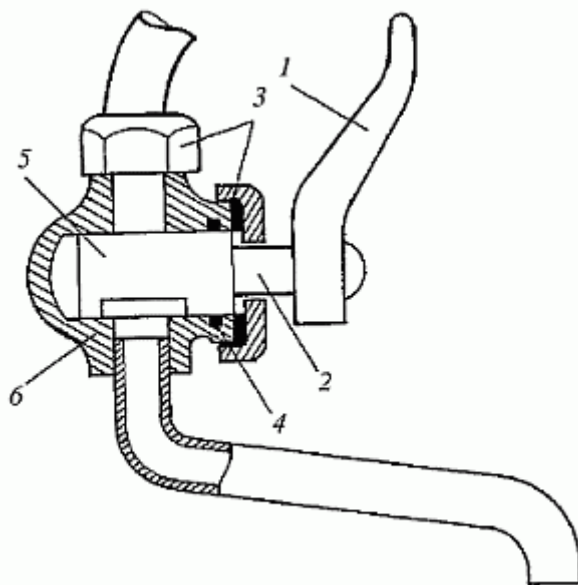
Устройство смесителя с пробочным переключателем «душ-излив»: 1 – ручка переключателя; 2 – шток; 3 – накидная гайка; 4 – стопорная шайба; 5 – пробка; 6 – корпус
